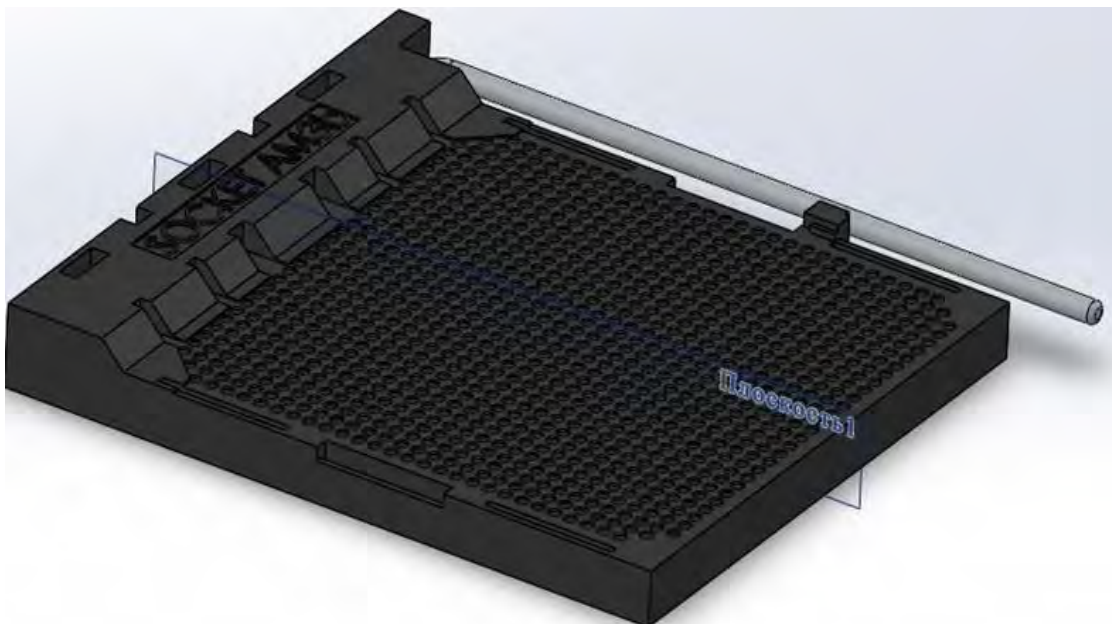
3-D модель процессорного гнезда AM3+ Socket
